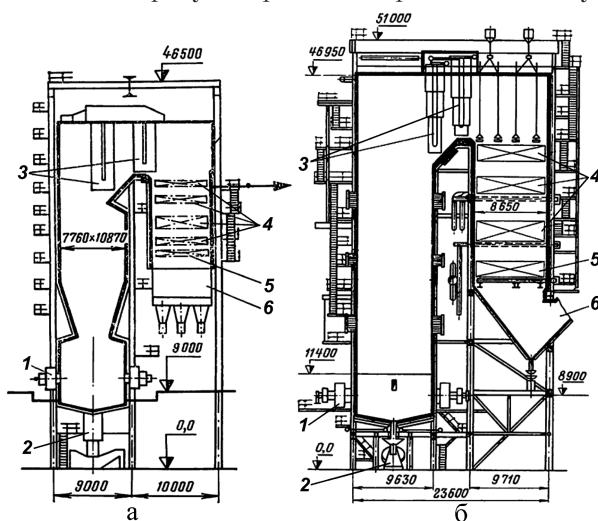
Схема котлоагрегатов ТПП-210А (двухкорпусный, на рисунке показан один корпус) (а) и ТПП-312А (однокорпусный) (б): 1 — горелка; 2 — шлакоудаляющий транспортер; 3 — ширмовый пароперегреватель; 4 — конвективная часть пароперегревателей; 5 — экономайзер; 6 — короб выхода дымовых газов, идущих к выносным регенеративным подогревателям воздуха (РВП).
